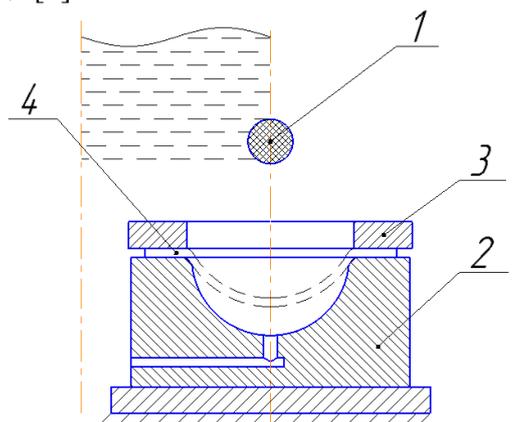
Обобщенная схема установки для взрывной штамповки: 1 – заряд взрывчатого вещества; 2 – матрица; 3 – прижимное кольцо; 4 – заготовка.
